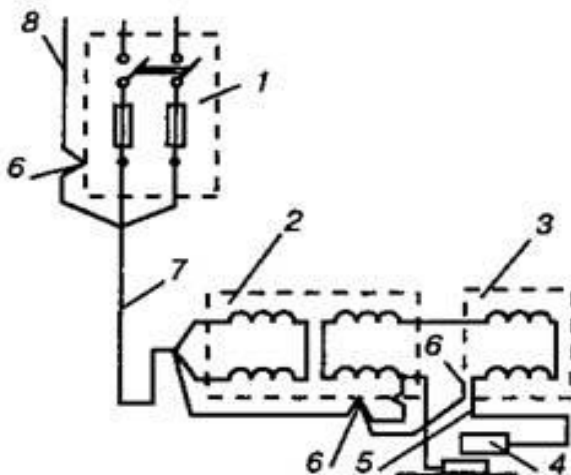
Схема подключения сварочного трансформатора:
